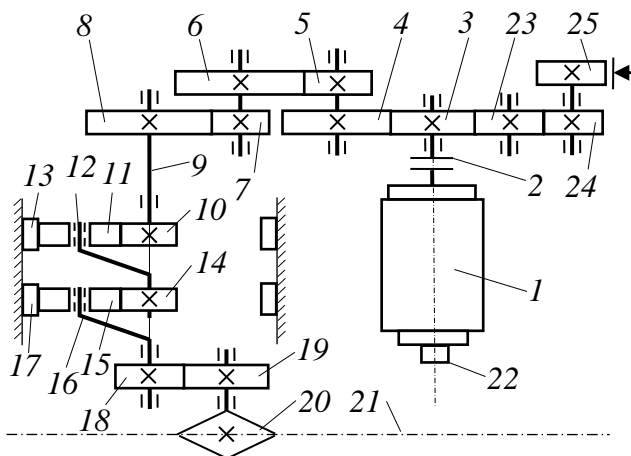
Кинематическая схема механизма подачи очистного комбайна типа CL 300: 1 – электродвигатель подачи; 2 – муфта; 3–8 – зубчатые колеса цилиндрического редуктора (5 и 6 – сменные шестерни); 9 – вал; 10–17 – зубчатые колеса двухступенчатого планетарного редуктора (12 и 17 – водила); 18 и 19 – колеса редуктора цевочного колеса 20; 21 – цевка; 22 – датчик оборотов двигателя; 23 и 24 колеса редуктора привода тормоза 25
